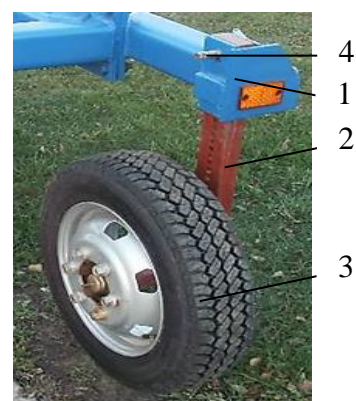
Опорное колесо с механизмом регулирования глубины обработки орудия: 1 - кронштейн; 2 - стойка; 3 - опорное колесо; 4 - рукоятка с эксцентриком.
